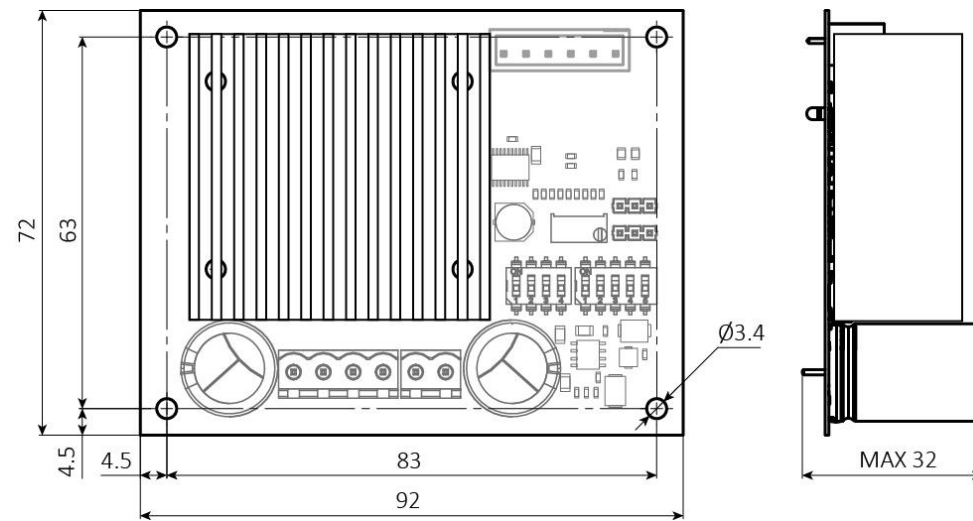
Габаритные и присоединительные размеры драйвера шагового двигателя SMD-8.0.
